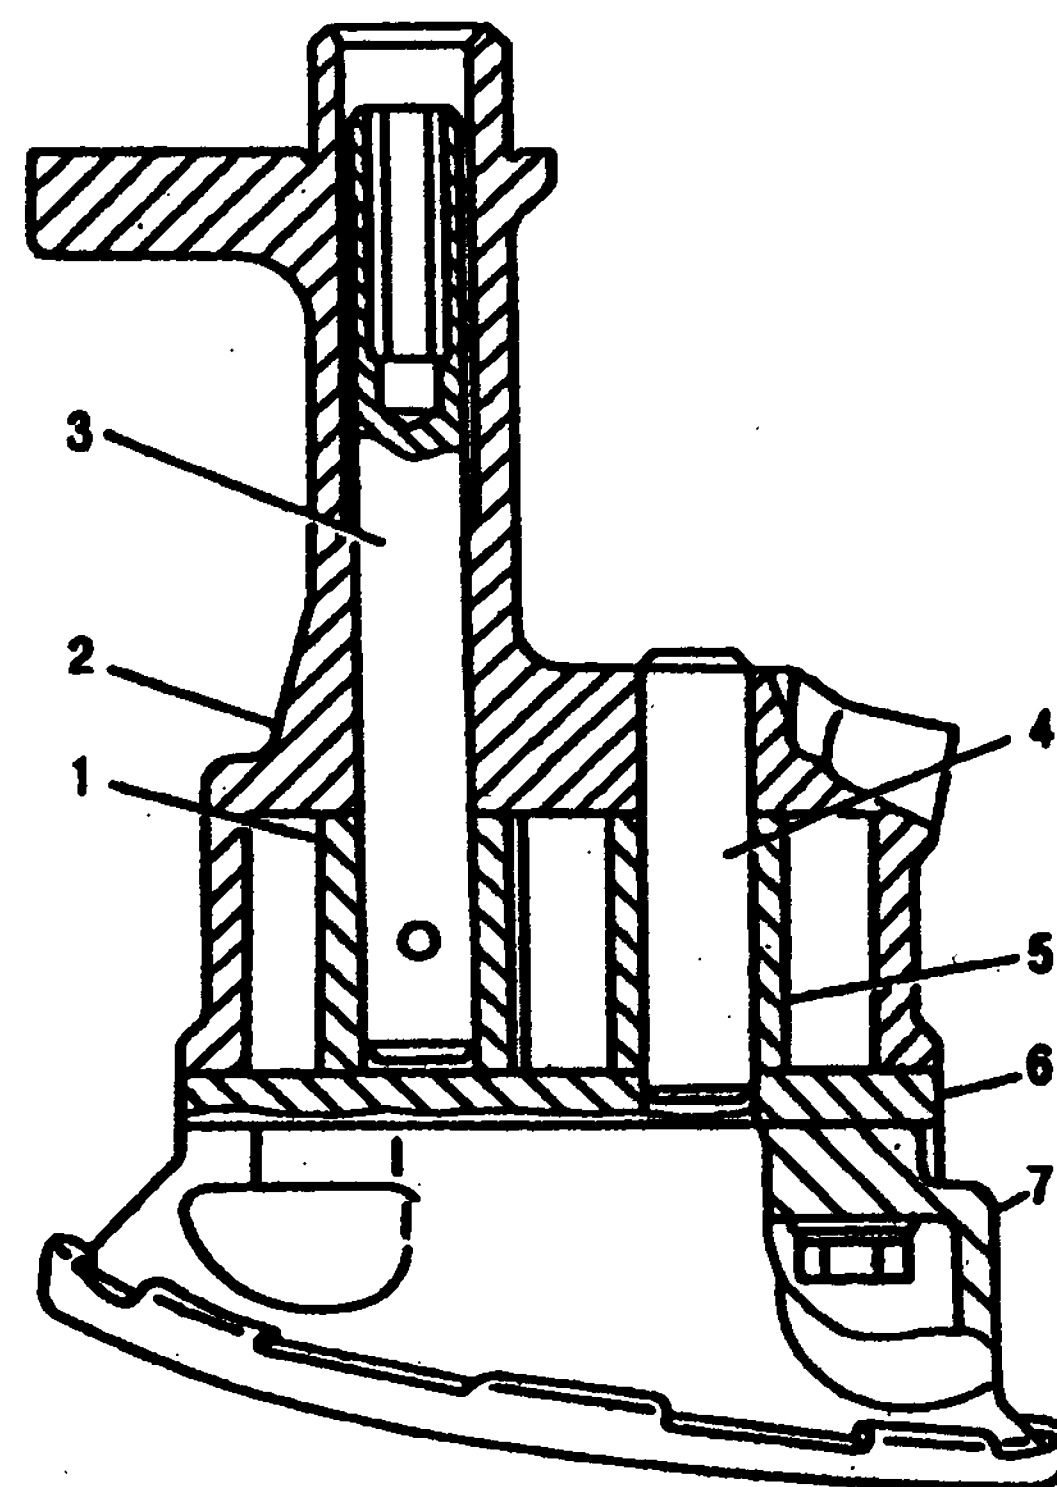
Масляный насос: 1 - ведущая шестерня; 2 - корпус; 3 - валик; 4 - ось; 5 - ведомая шестерня; 6 - перегородка; 7 - приемный патрубок с сеткой
